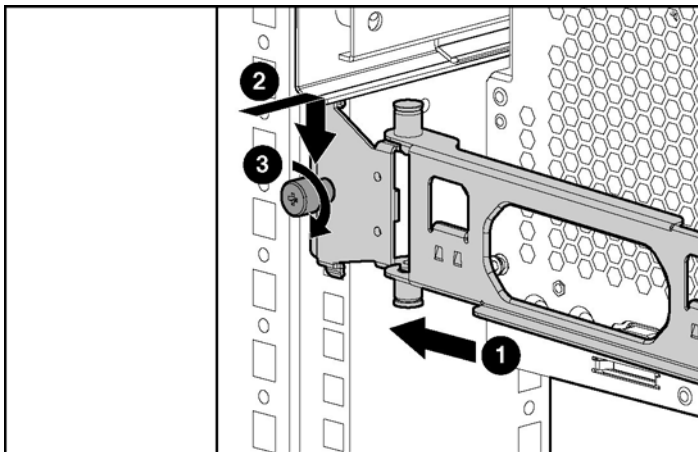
Befestigen des Kabelführungsarms am Rack mit eckigen Montageöffnungen
